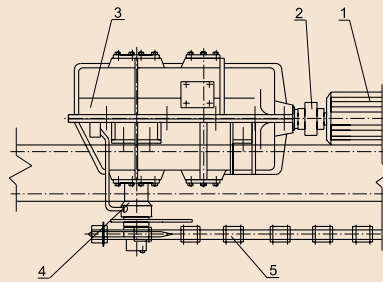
Привод подвесного цепного конвейера на базе коническо-цилиндрического редуктора КДВ-250М:
